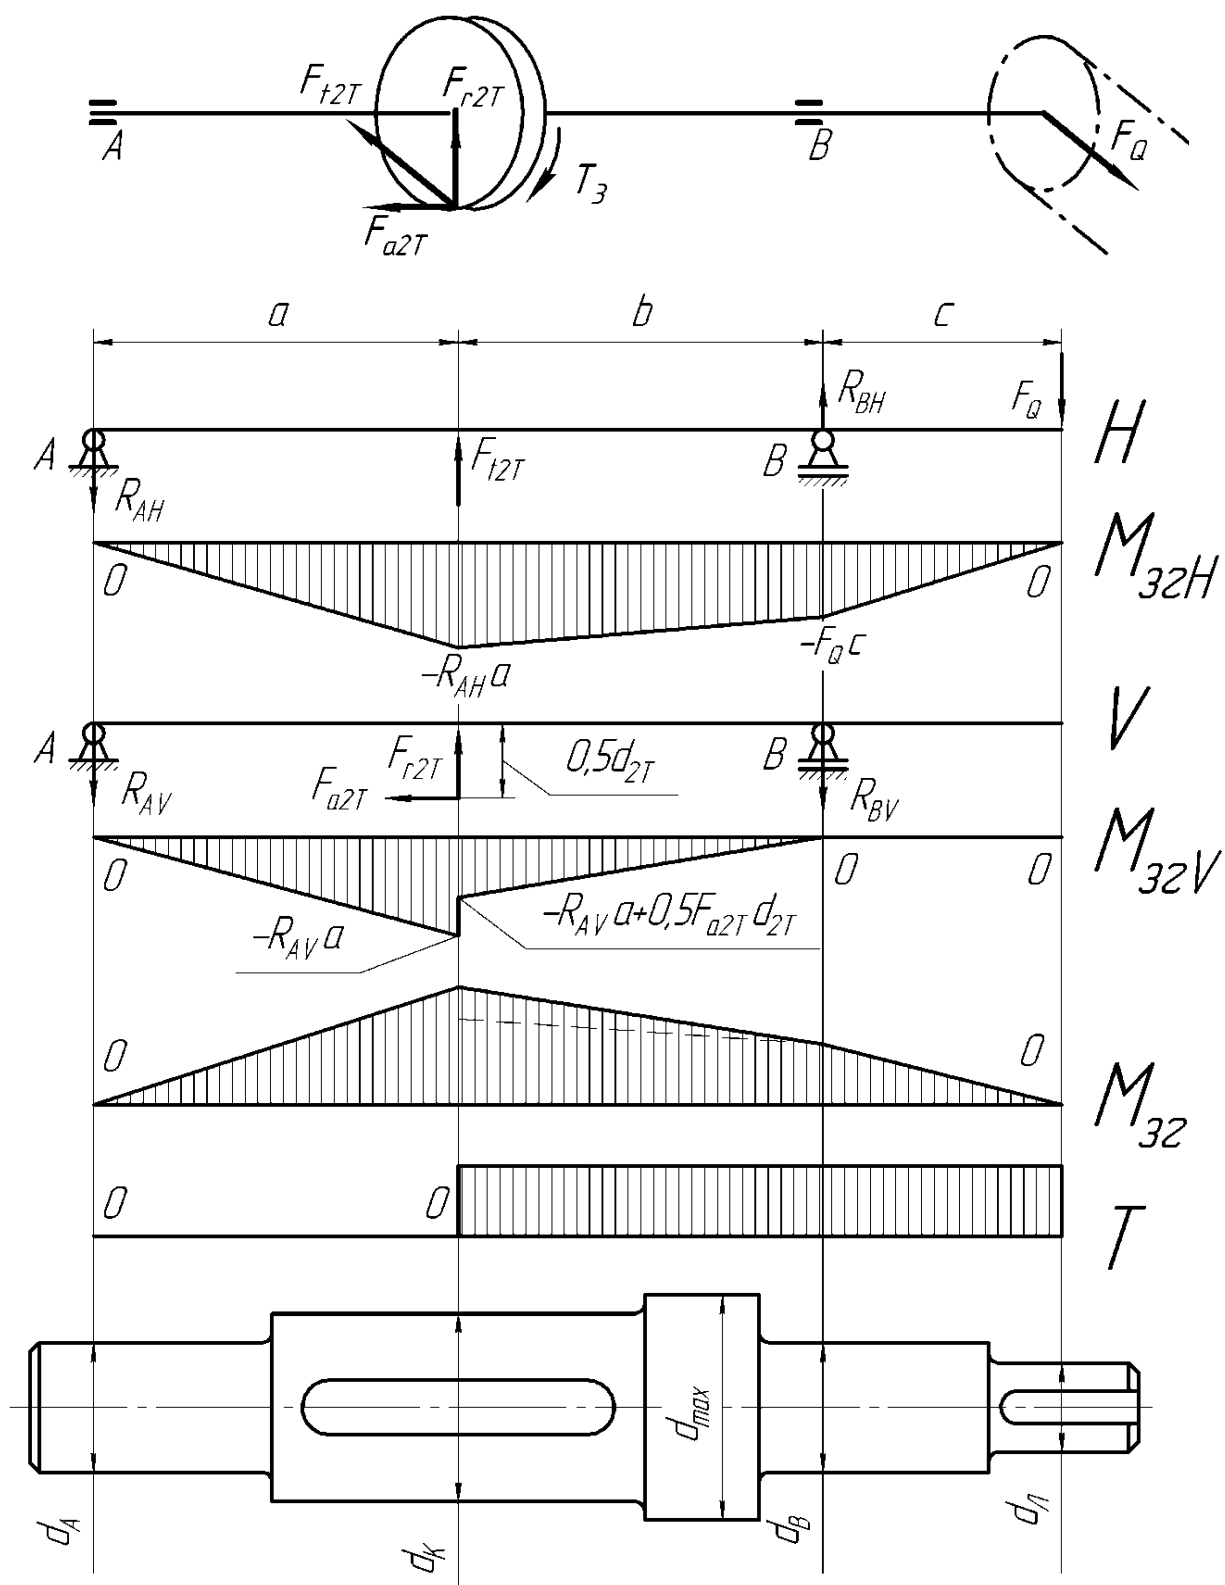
Розрахункові схеми, епюри згинальних і обертаючого моментів та ескіз веденого вала циліндрично-черв'ячного редуктора
